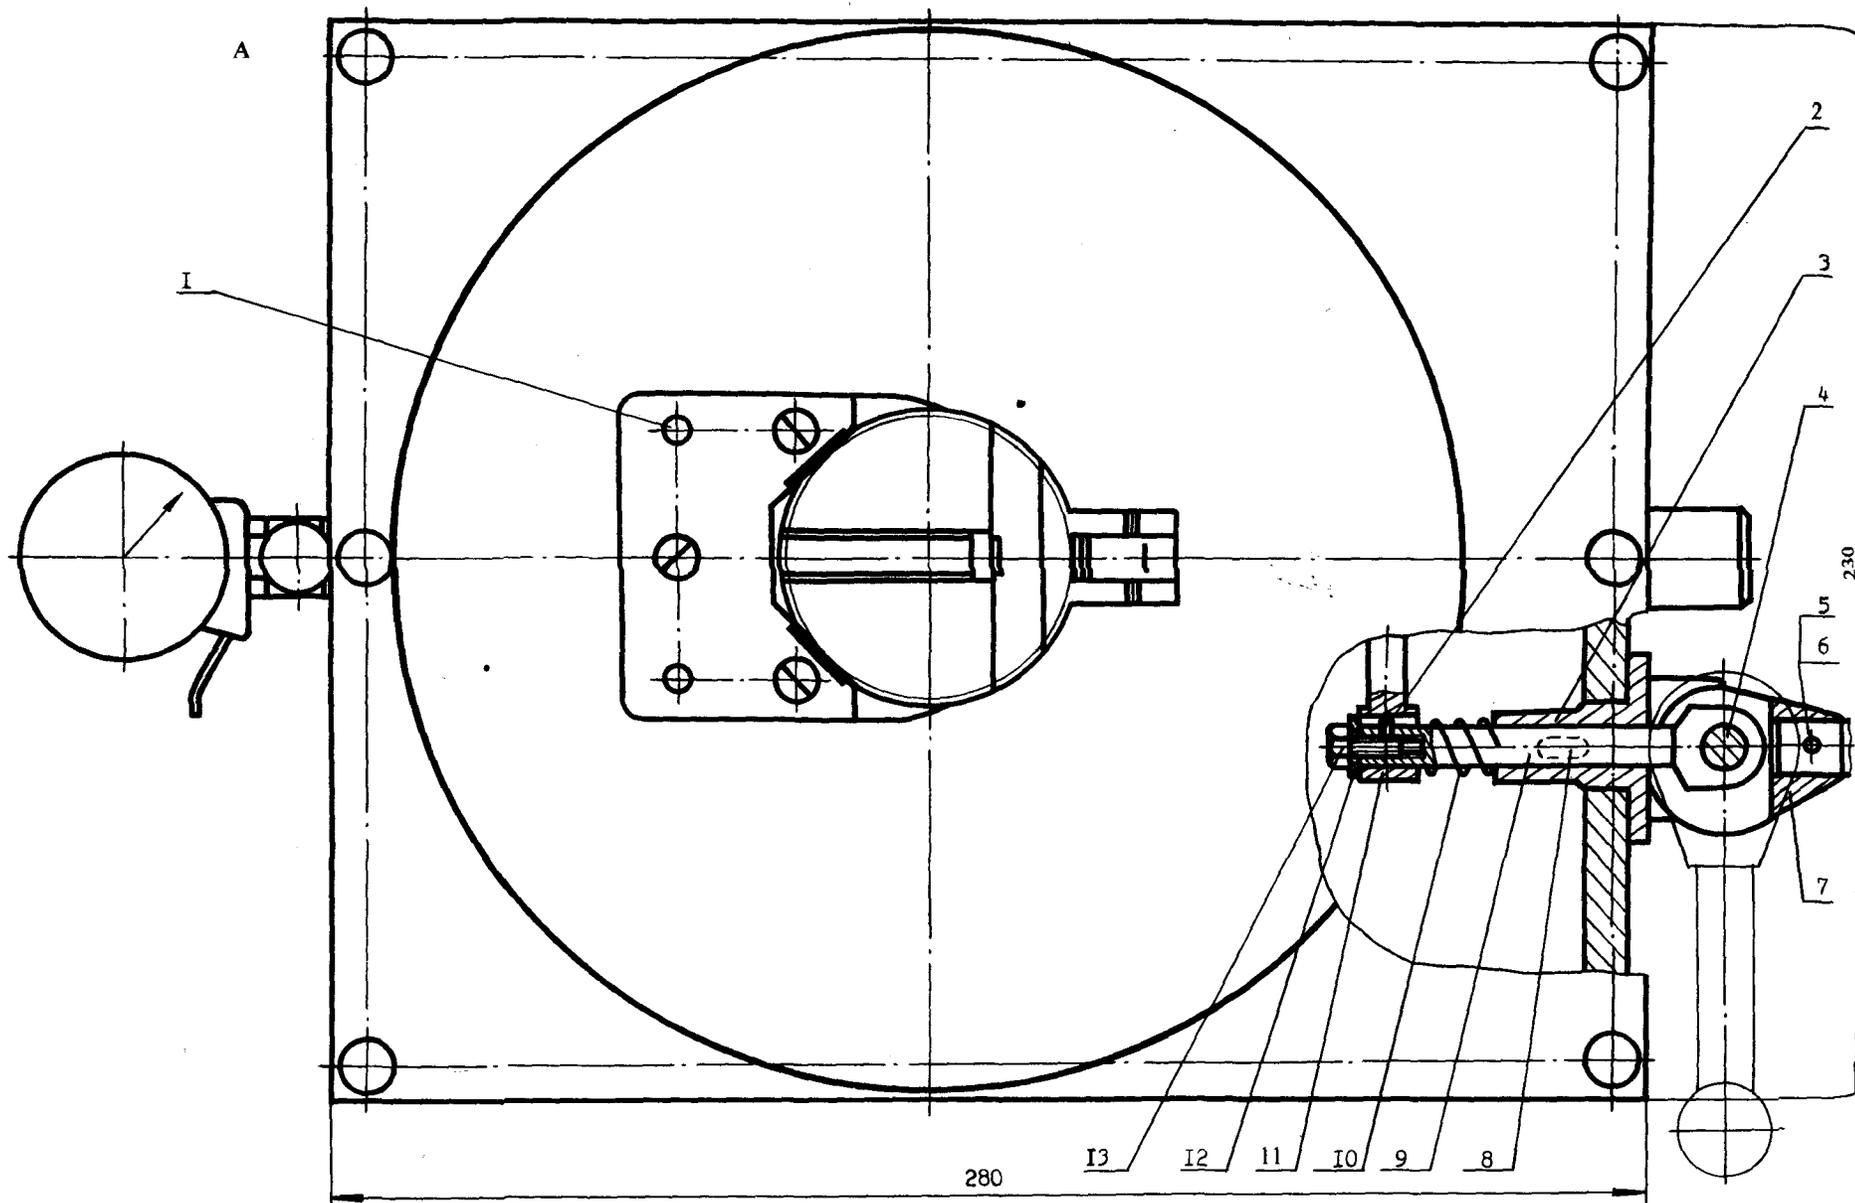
Контрольное приспособление для ступенчатого диска (вид А на рис. 2.11):
